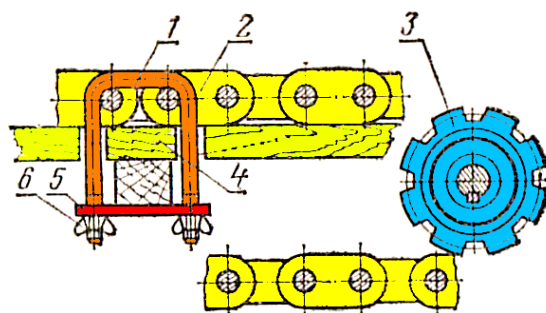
Приспособление для соединения цепи транспортера ТВК-80А:
